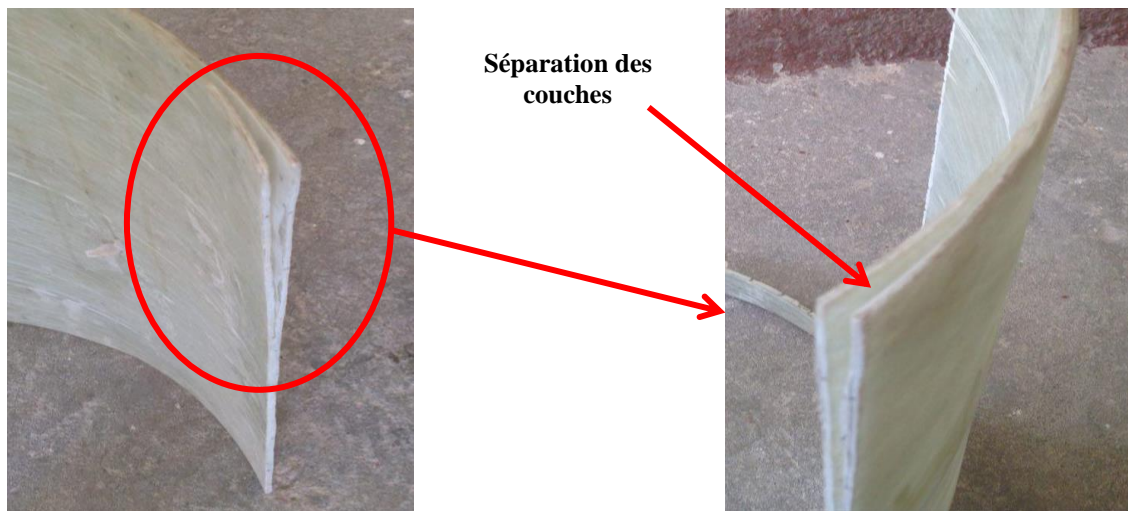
Séparation des couches pendant le découpage des éprouvettes DCB.
